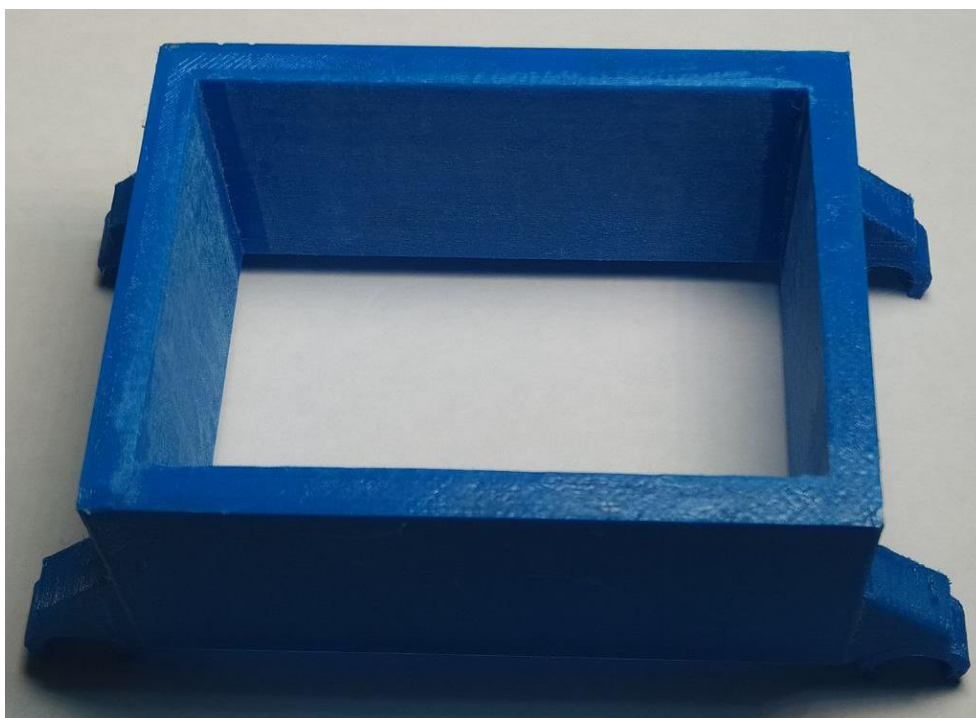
Зовнішня частина корпусу ванни для фотополімеру
